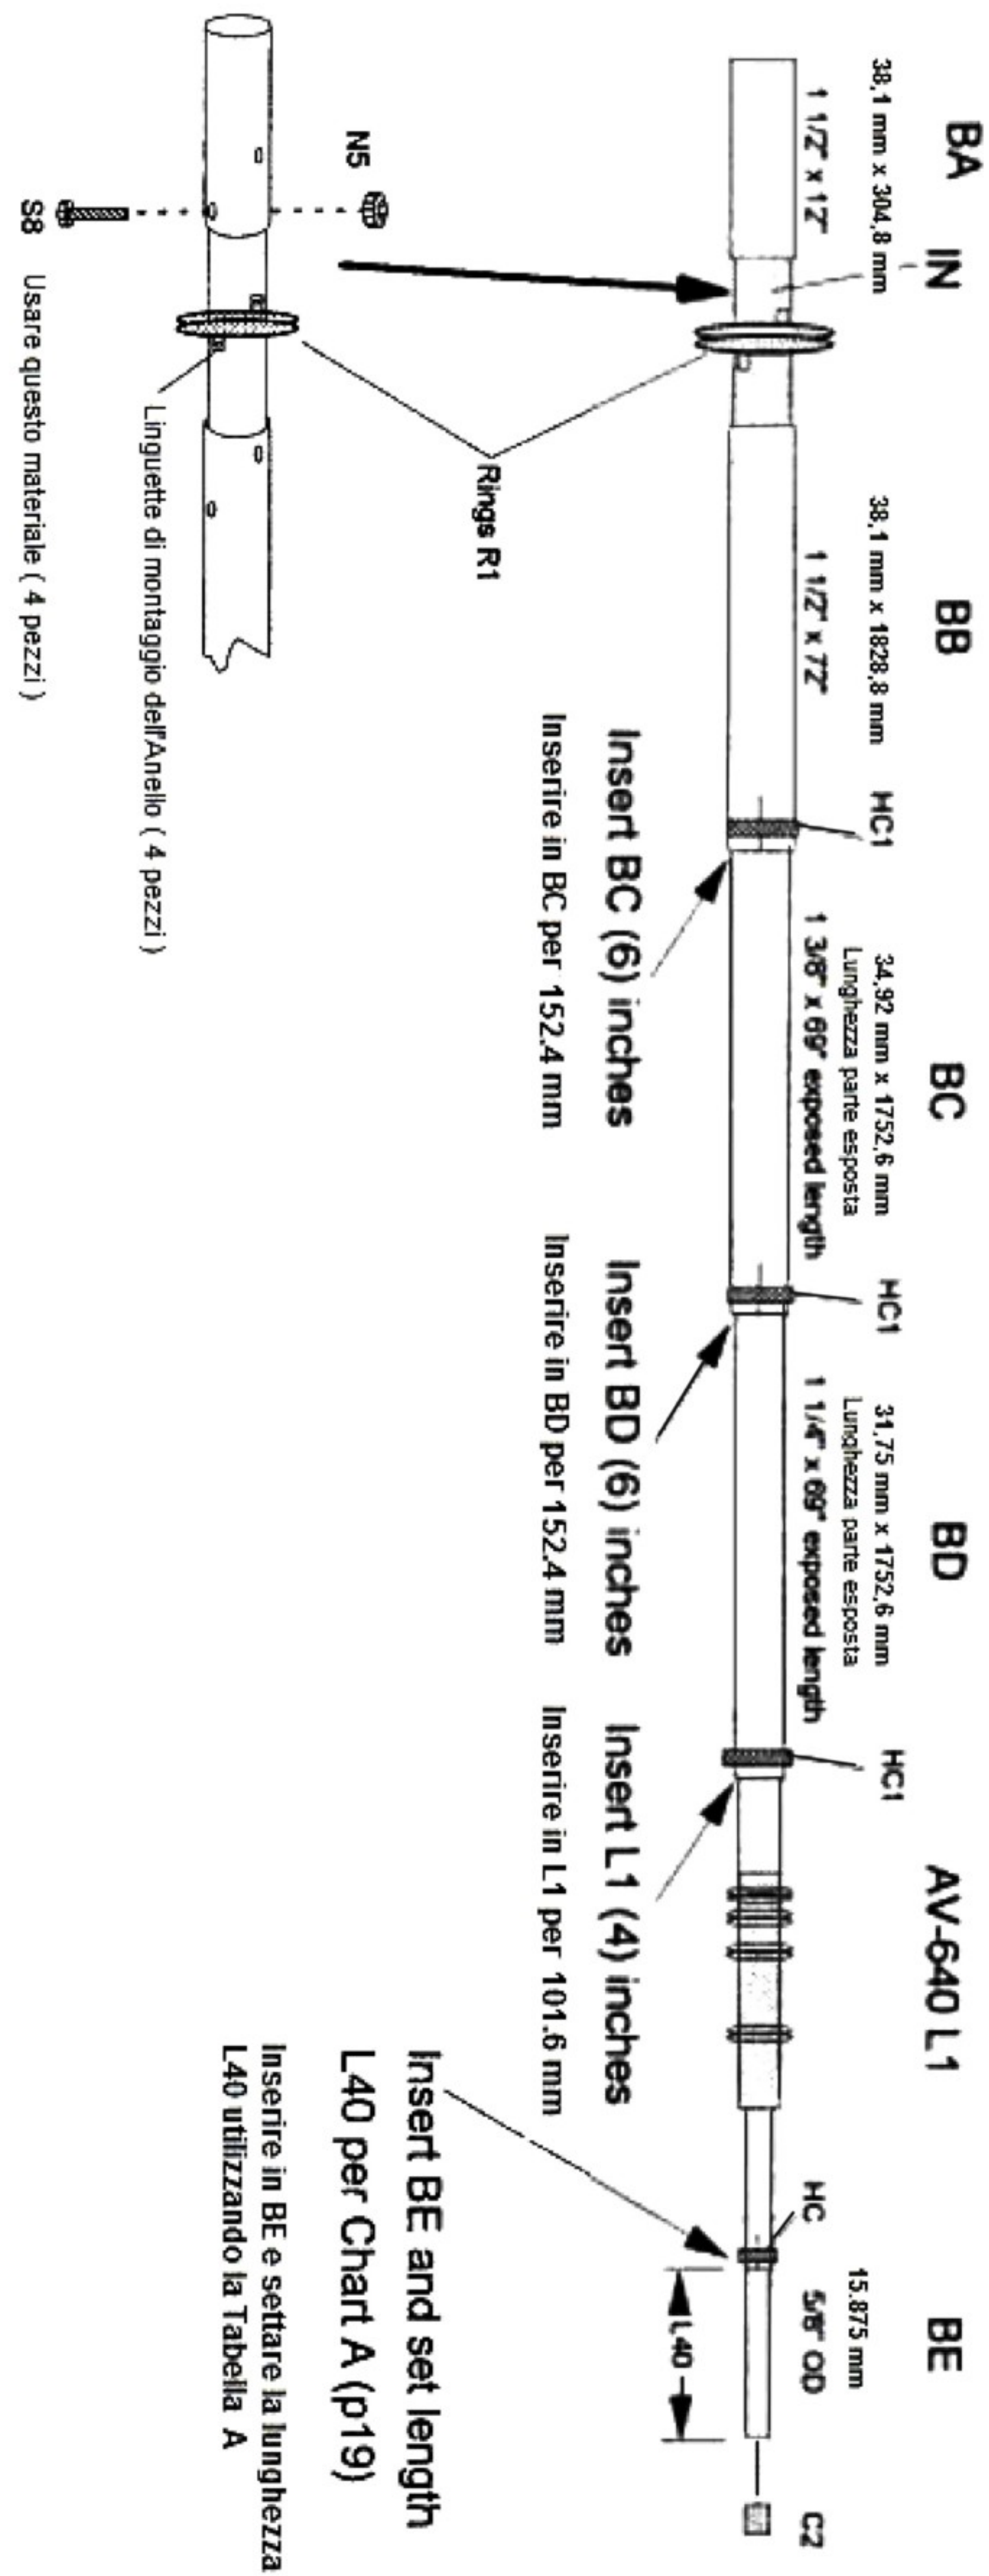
FIGURA B - Assemblaggio Supporti di Base degli Stub -
